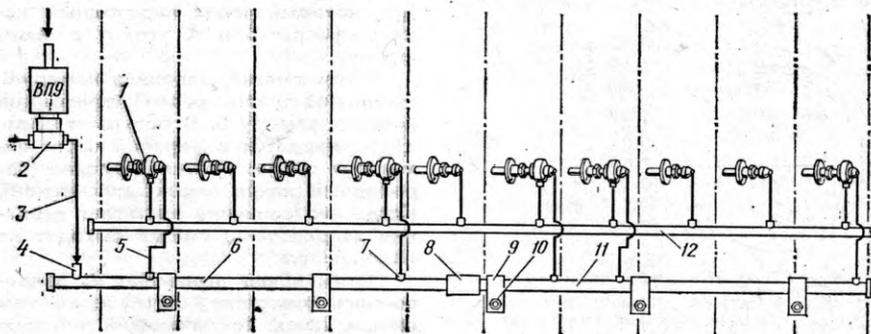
Схема установки устройства ПДФ-5 на дизеле: 1 — приставка-догрузатель форсунки; 2 — тройник; 3, 5 — воздушный трубопровод; 4 — штуцер подвода воздуха; 6, 11 — несимметричные половины воздушного коллектора; 7 — штуцер отвода воздуха; 8 — втулка-муфта; 9 — скоба; 10 — болт; 12 — коллектор сливного топлива
